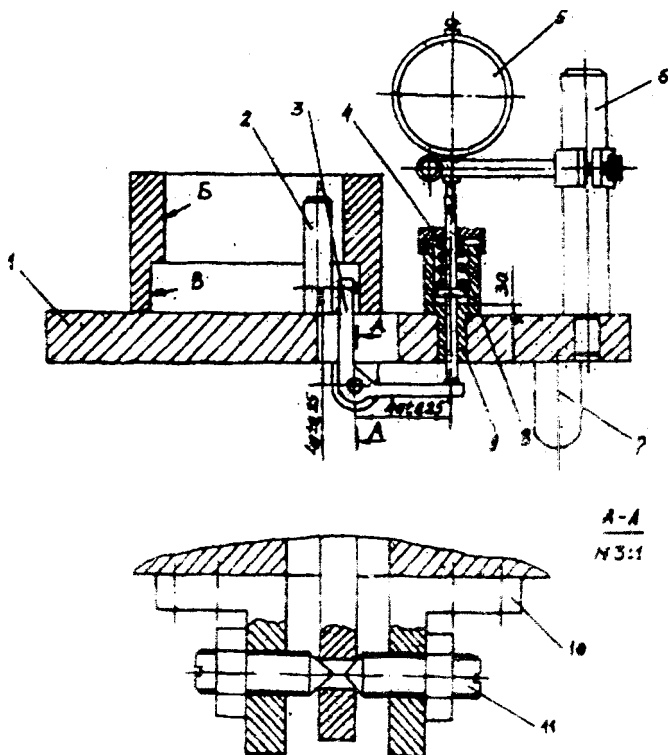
Контрольное приспособление для проверки радиального биения внутренних цилиндрических поверхностей
